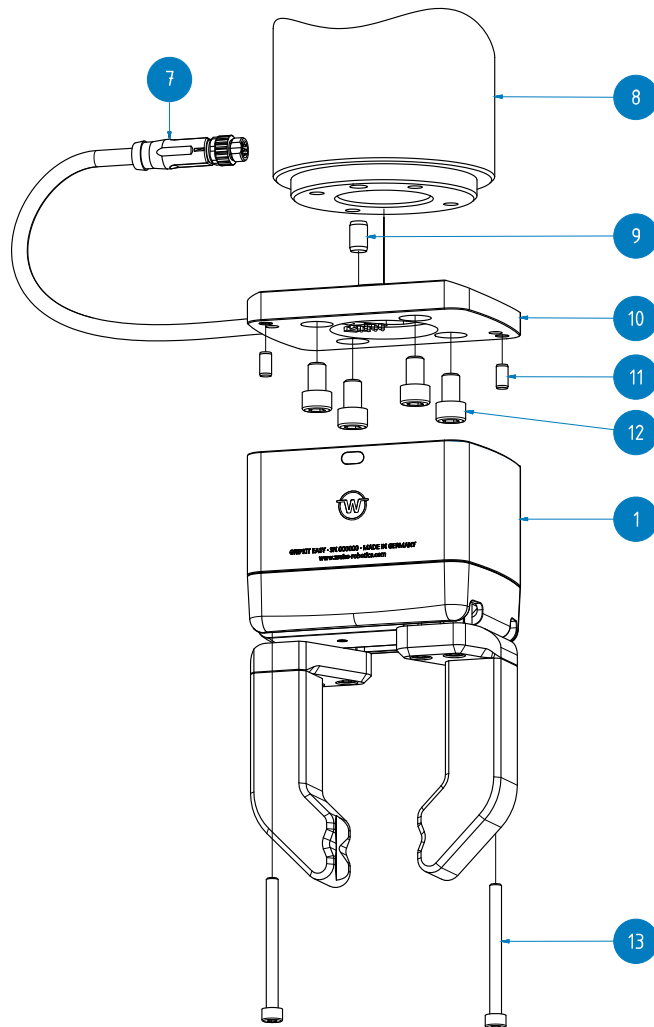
Montage des Greifmoduls am Roboterflansch
